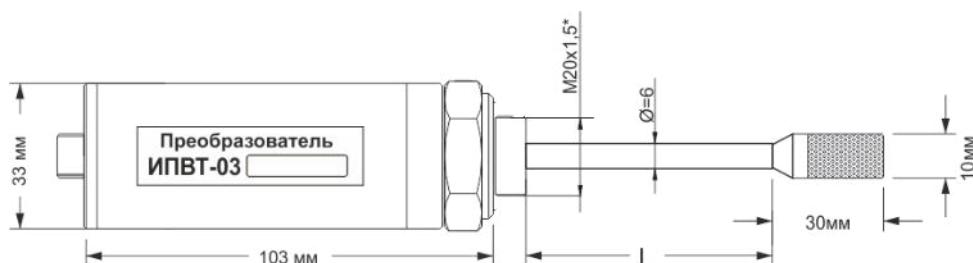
Измерительный преобразователь ИПВТ-03-06
